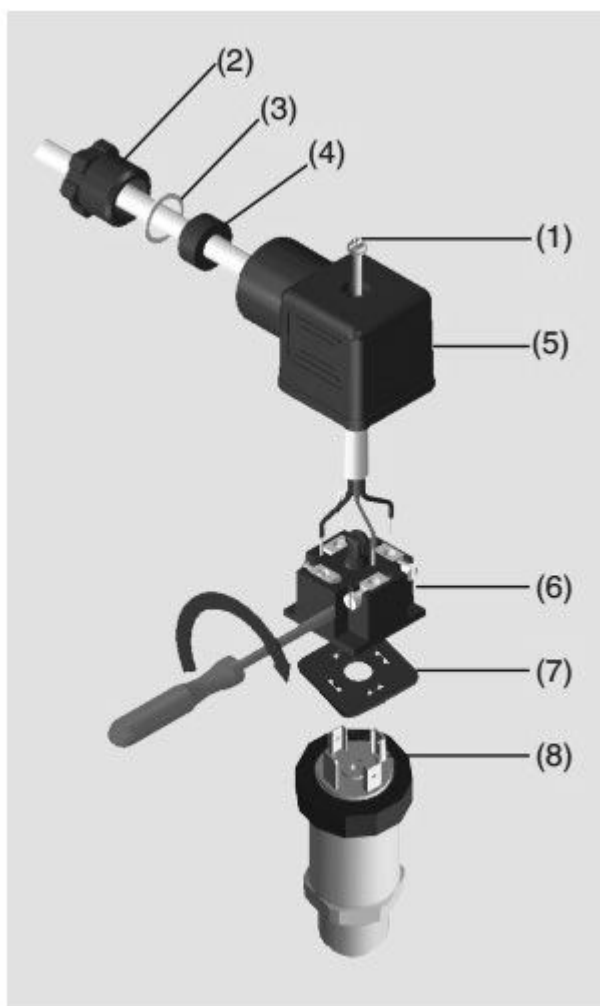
Схема сборки преобразователя давления S-10
